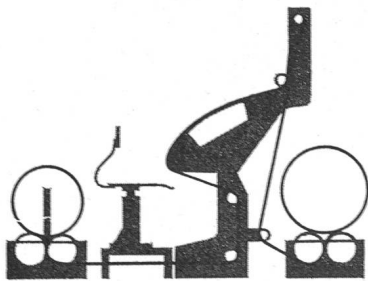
Vorschaumaschine P 6 (Maschinenbau Mengen)
